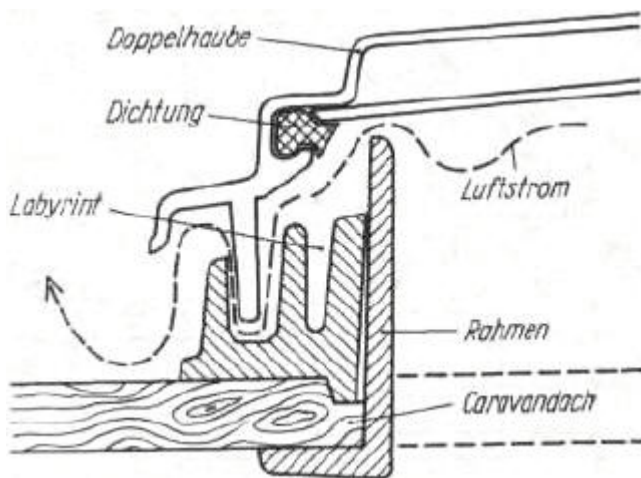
Konstruktive Lösung der Abdichtung einer Dachhaube mit Zwangsventilation
